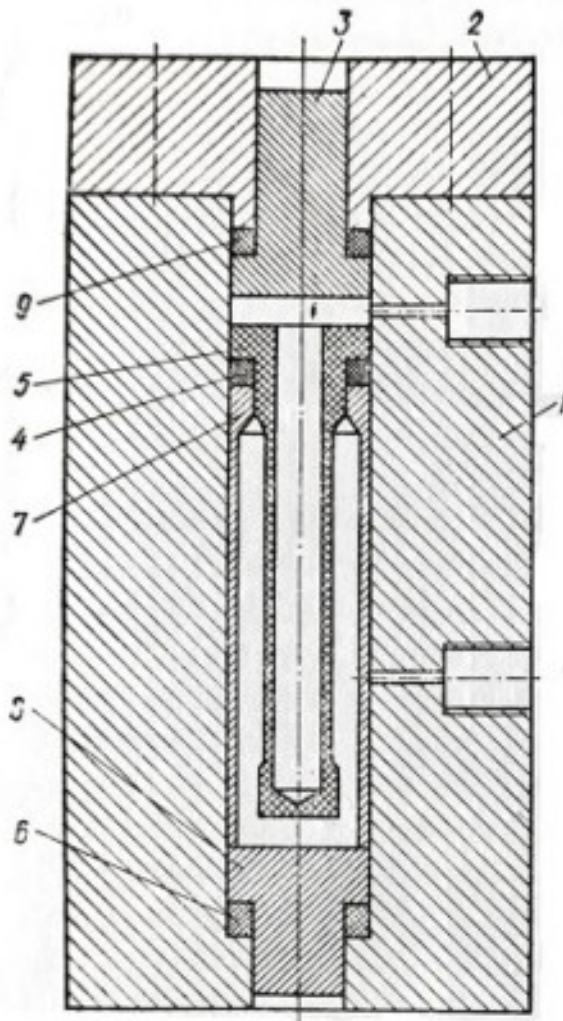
Схема установки для испытания трубчатых образцов:
